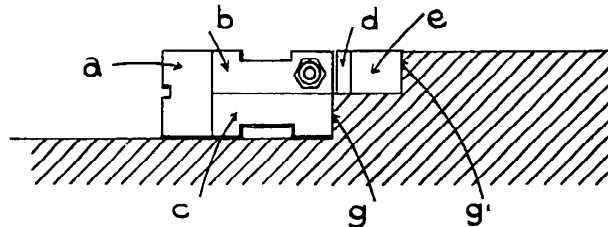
ENSEMBLE DES DIVERS COINS, VUS EN BOUT.
